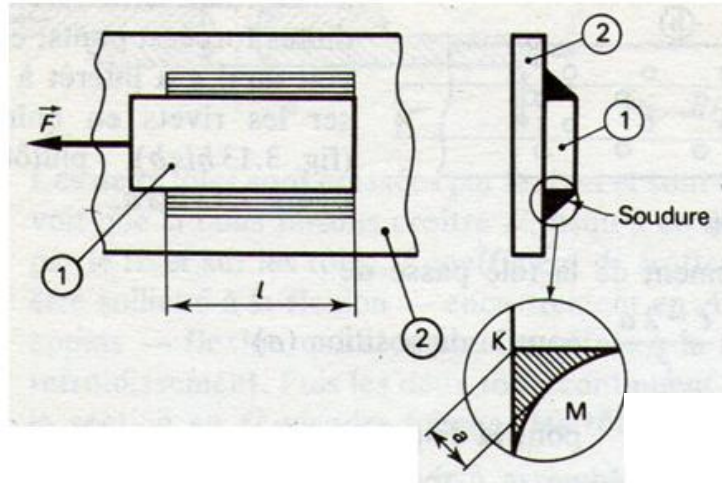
Exemple d'une soudure d'angle.
